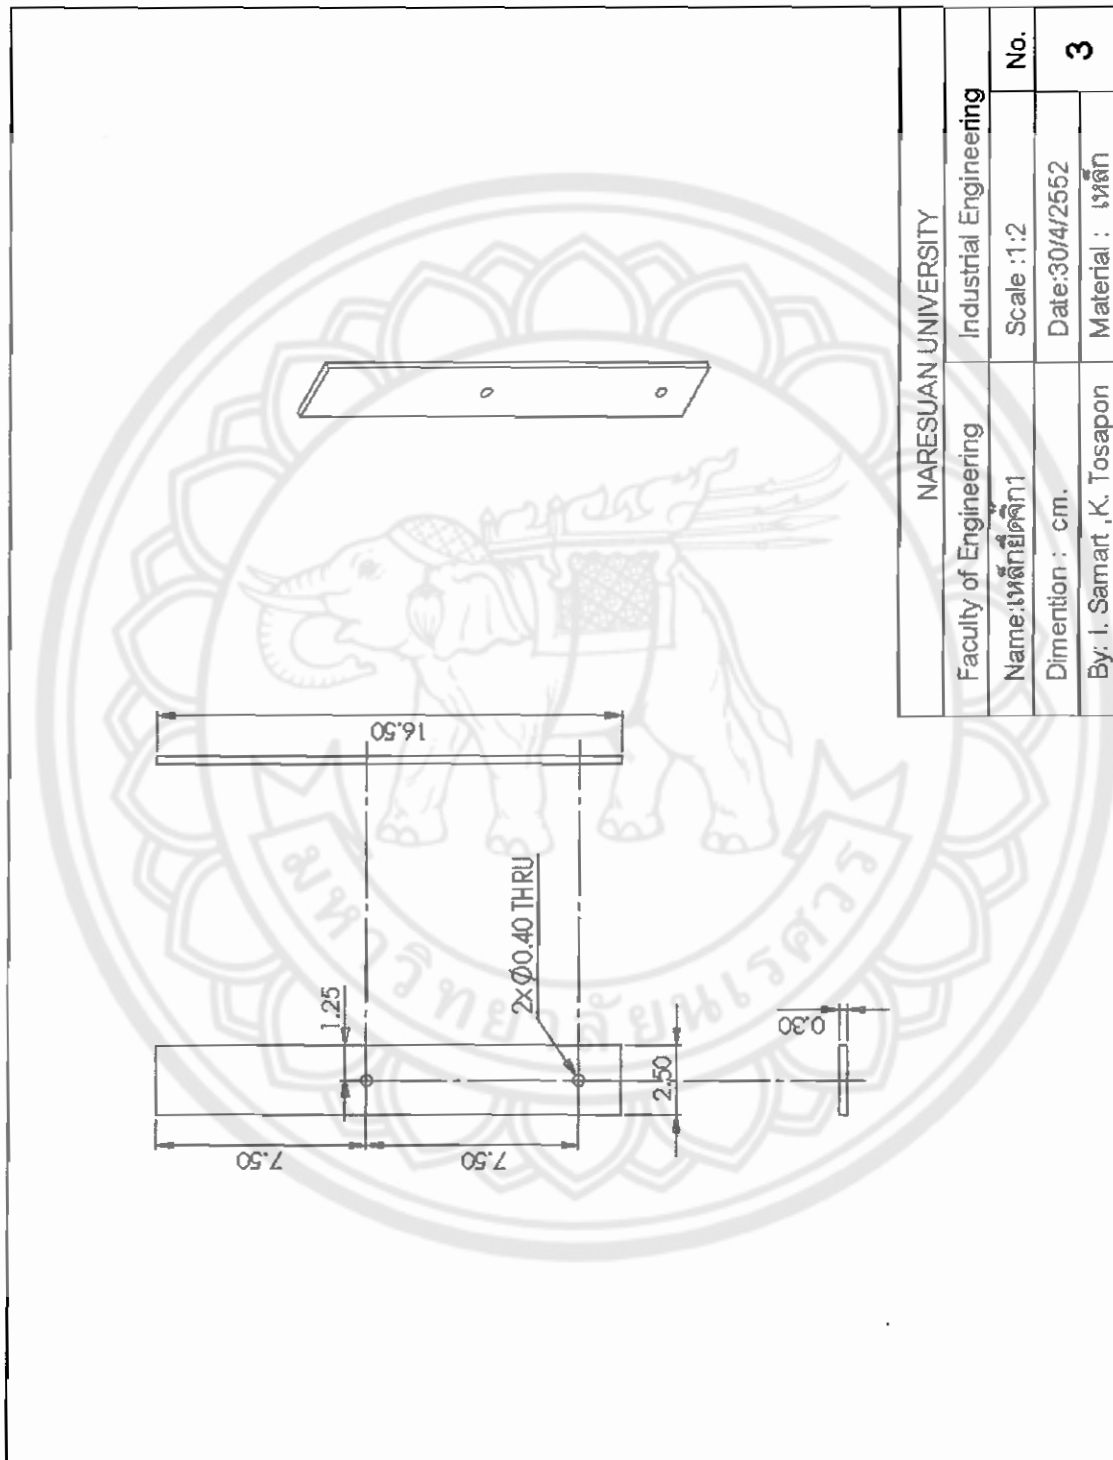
แสดง Assembly Drawing จิ๊กตั้งมือ
